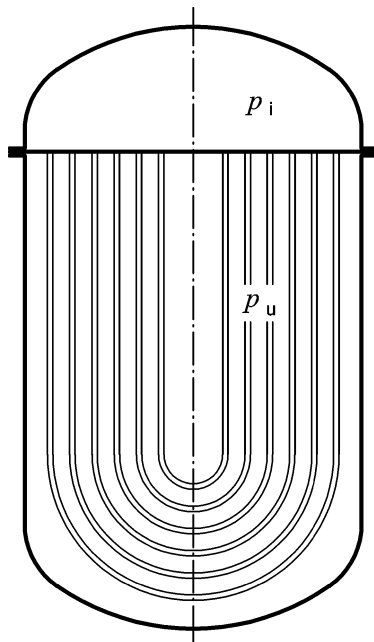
Runde, ebene, vollberohrte Platten mit rückkehrenden Rohren
